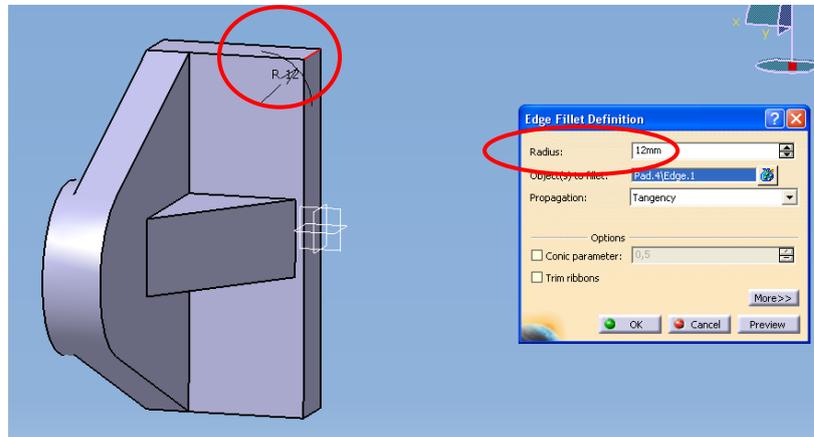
Cuadro de diálogo edge fillet definition, el valor correcto de la casilla radius y la esquina superior seleccionada.
